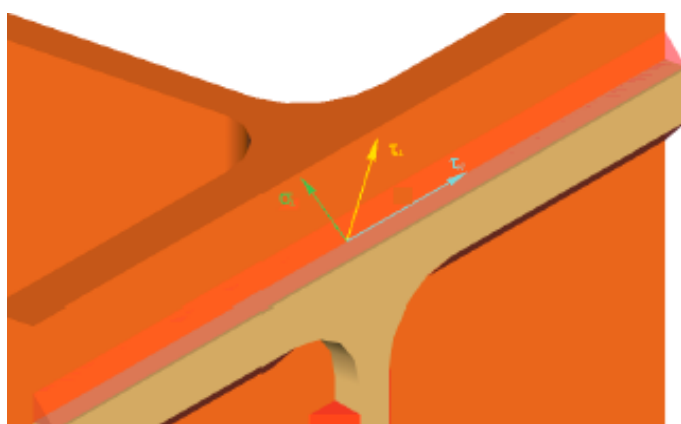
Descomposición de tensiones en cordón de soldadura
